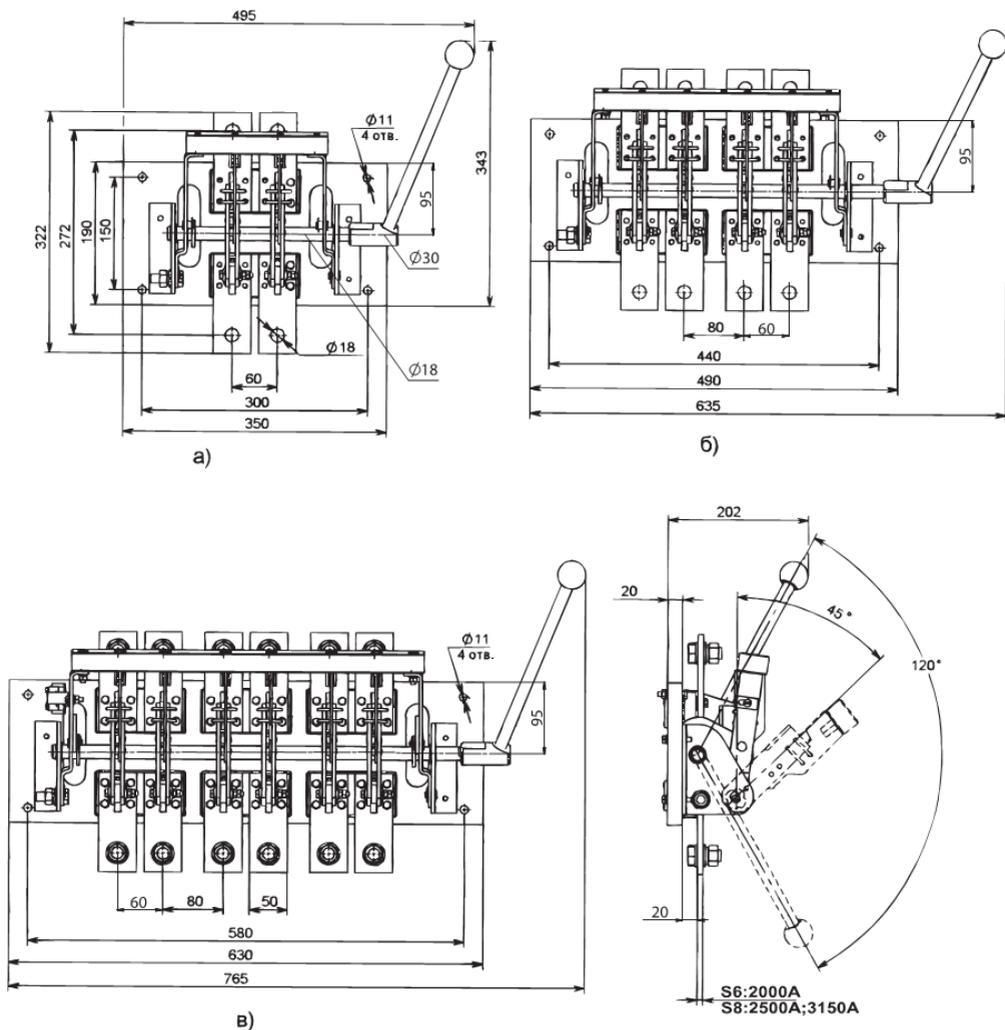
Разъединитель РЕ19 с боковой рукояткой, заднего присоединения шин
